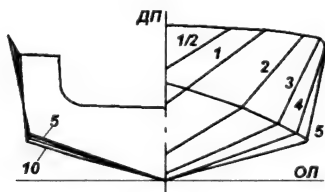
Теоретический корпус мотолодки «Москва-2»
